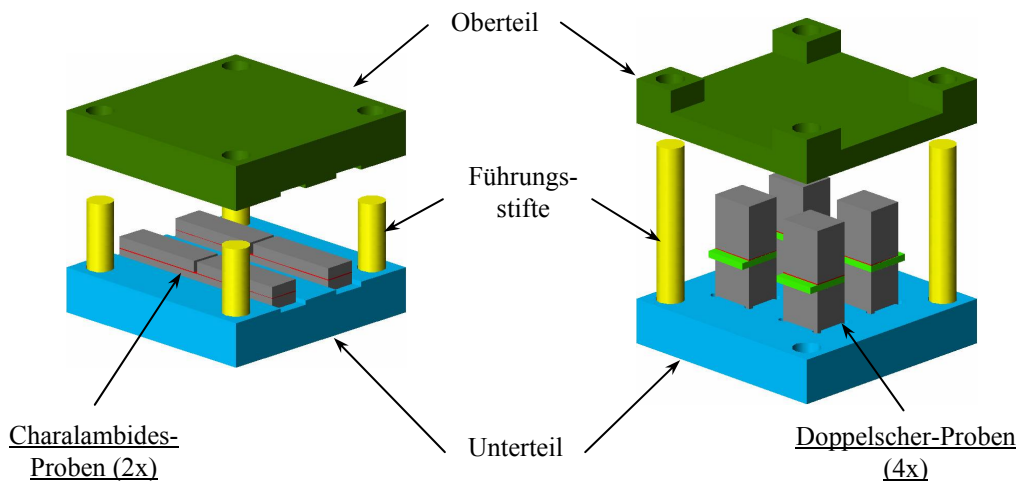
Schematische Zeichnung der Lötwerkzeuge
